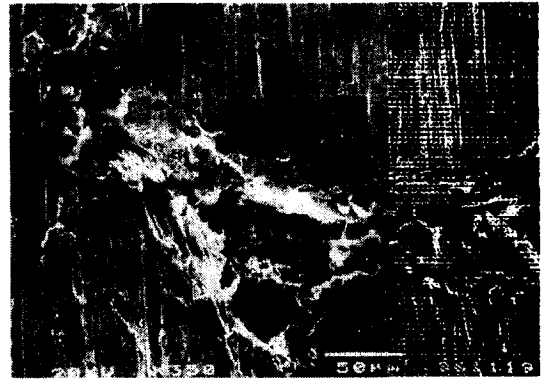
Fitting Anchor 파단면(미시적 관찰)
